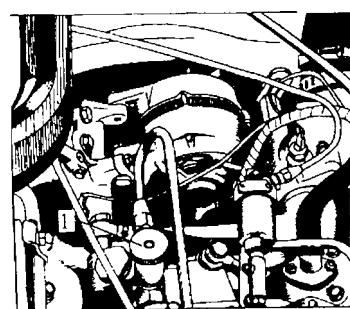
Топливоподкачивающий насос для двигателя 7403.10
